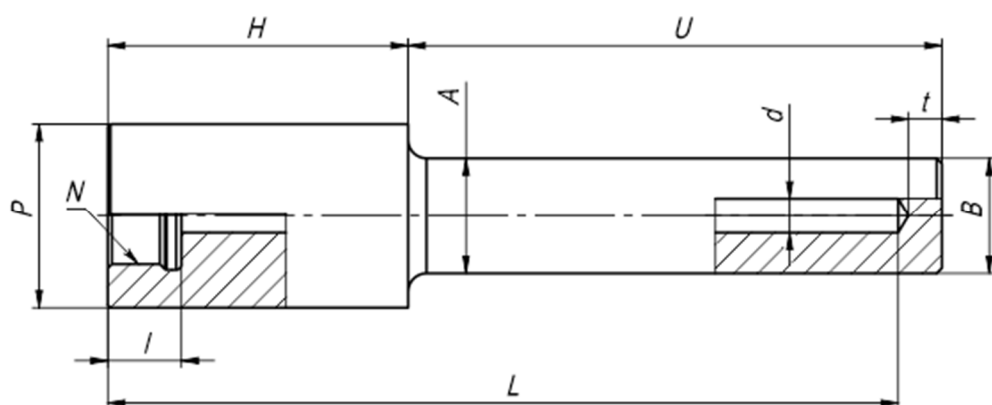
Гильза под приварку через адаптер (Socket Weld), цельноточёная, прямая, под неподвижный штучер.
